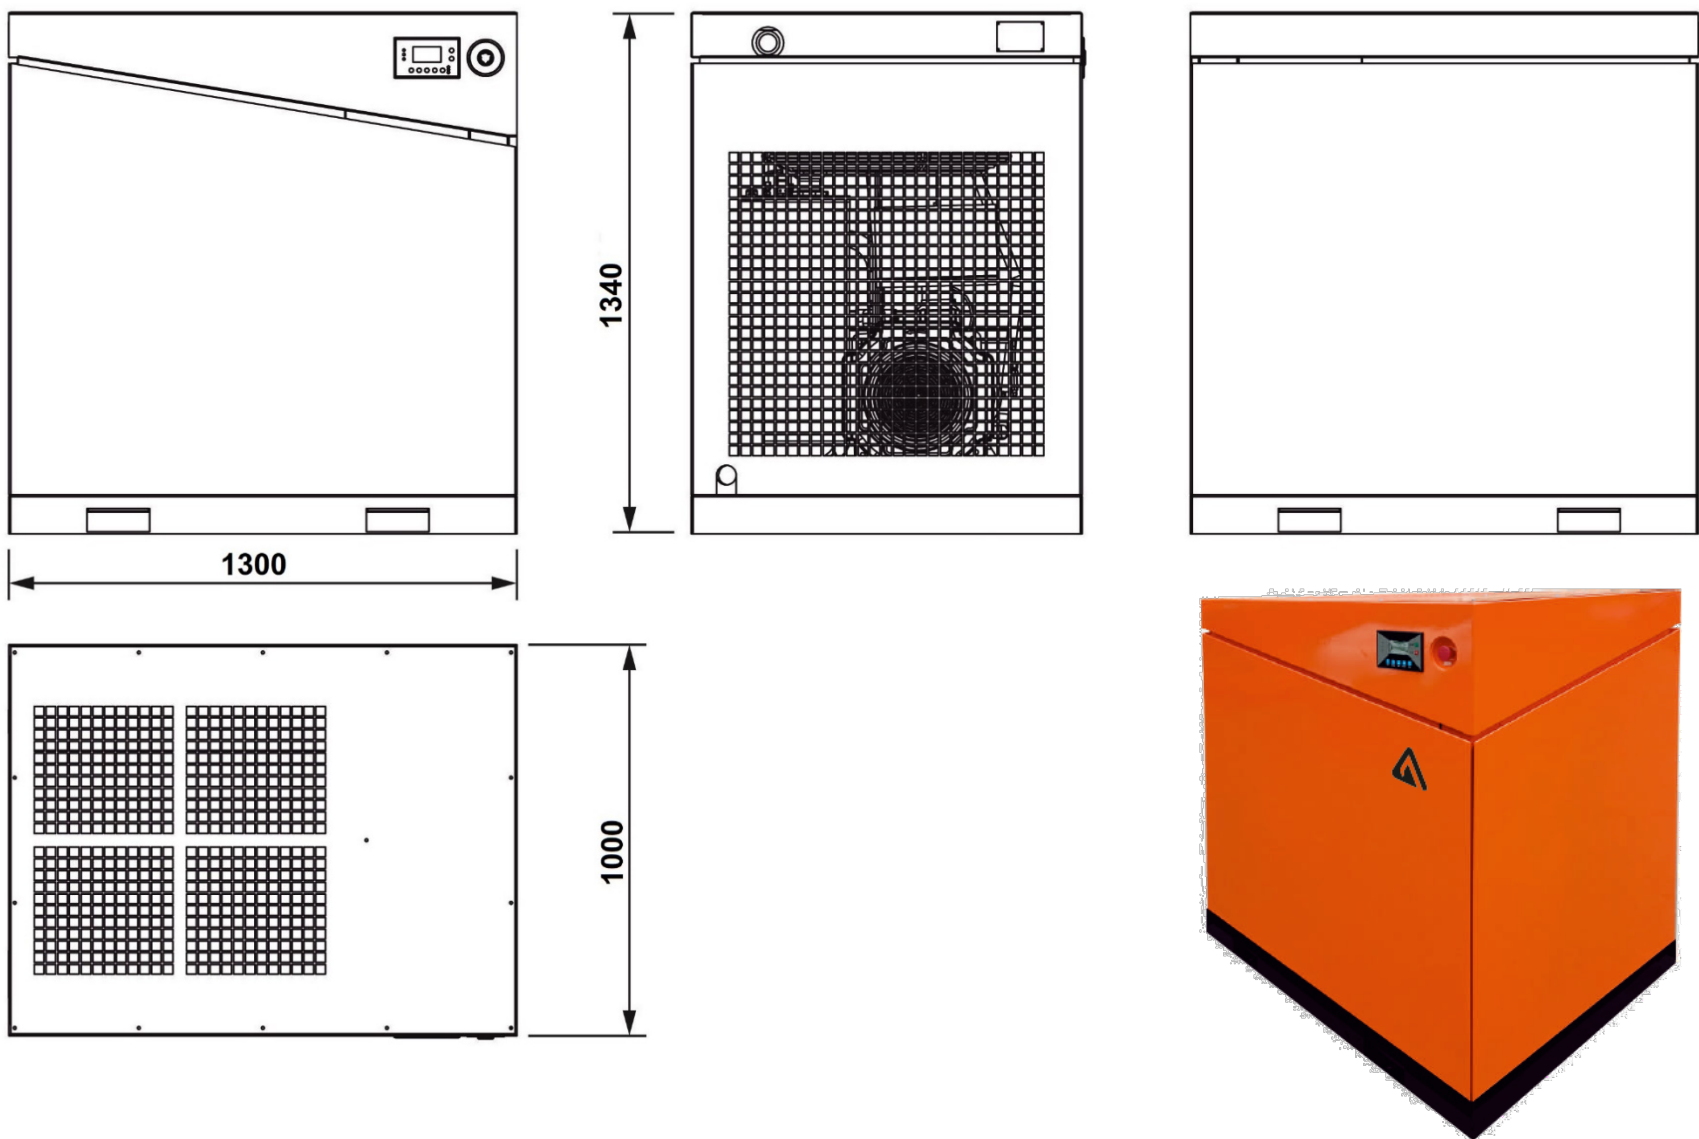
Общий вид, габаритные размеры станции компрессорной ЗИФ-СВЭ типа АРМ с двигателем 45 кВт
